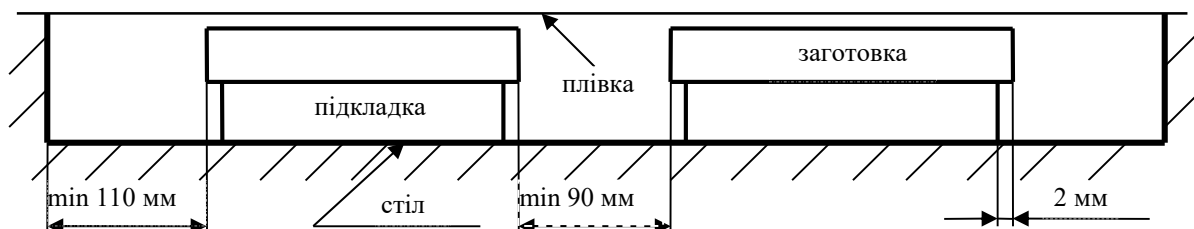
Розміщення заготовки на столі вакуумного верстата
